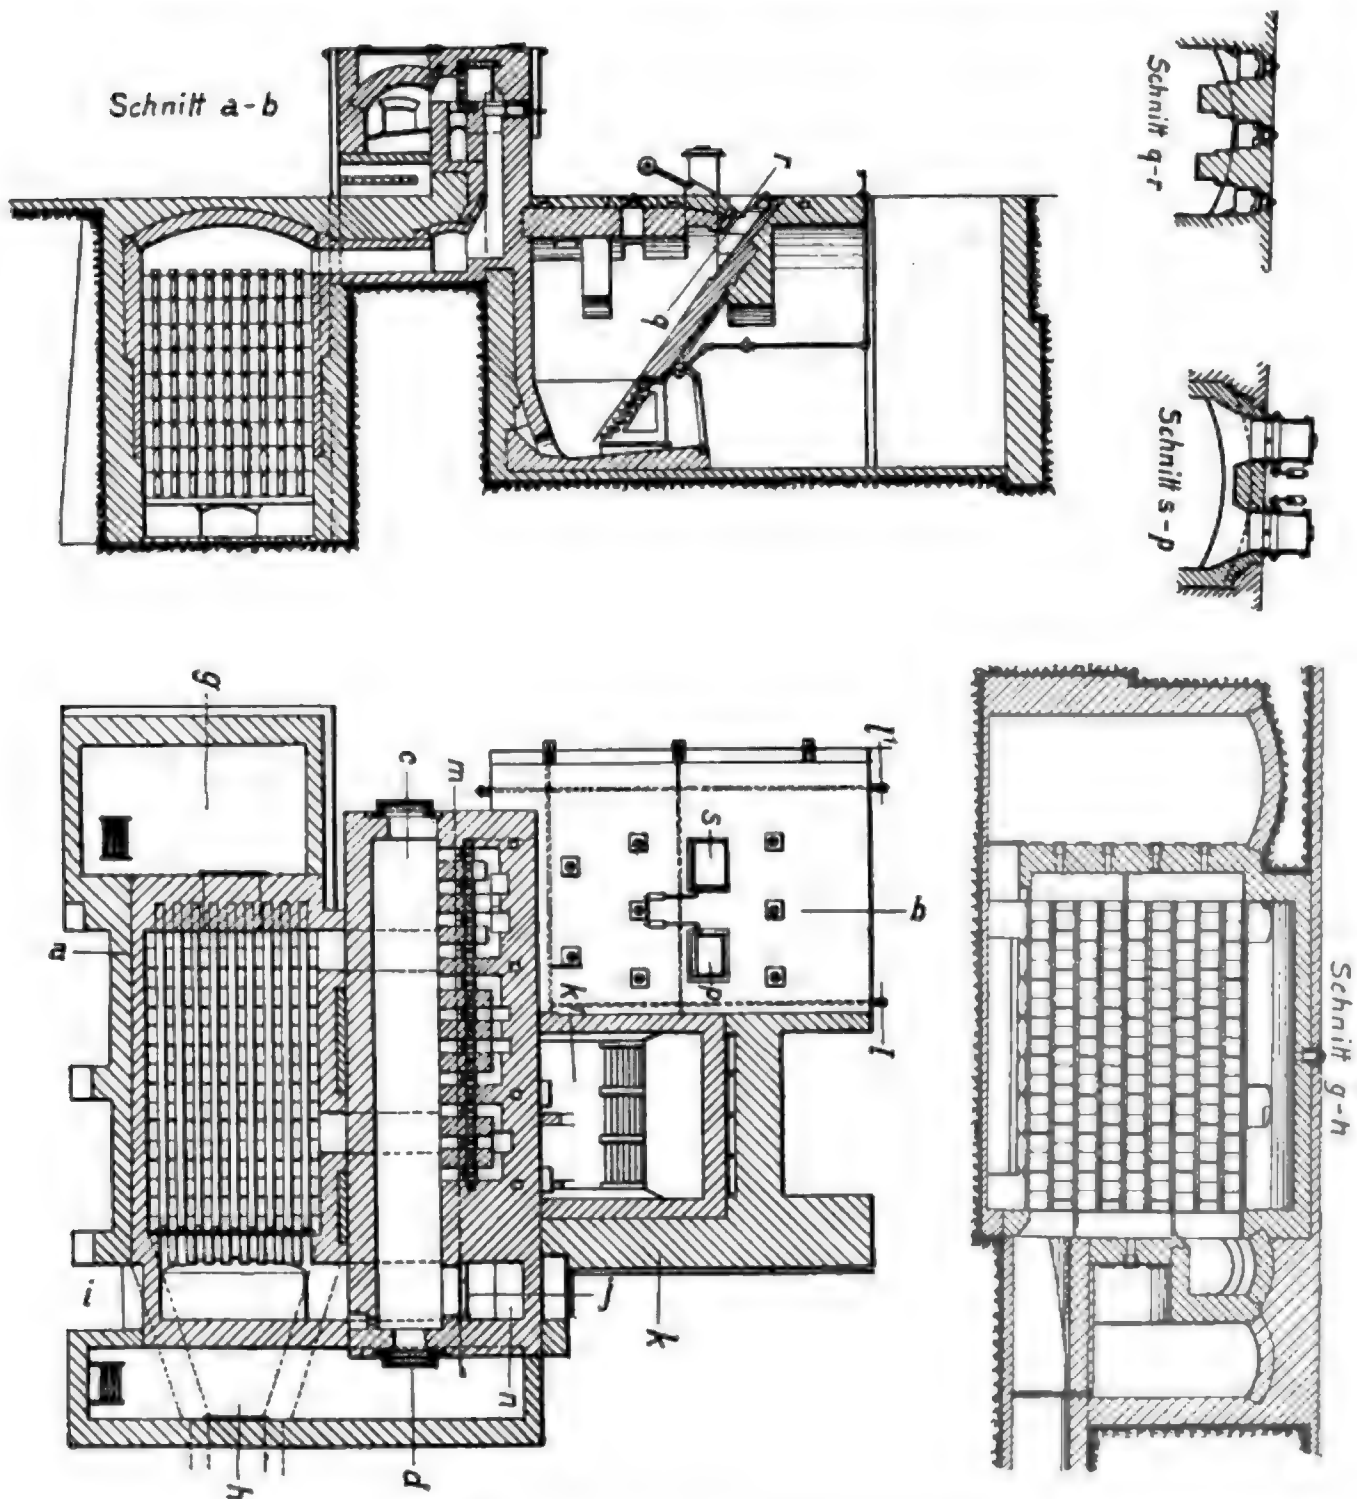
Rekuperator-Röhrenschweißofen.
